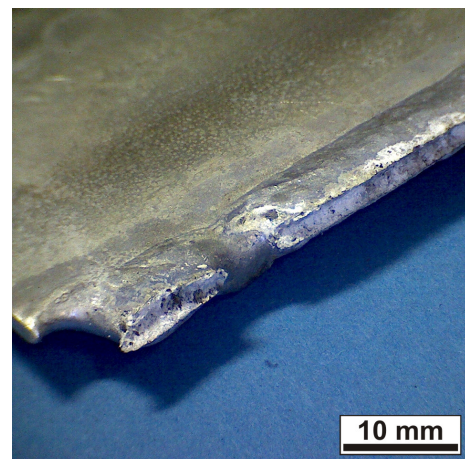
Unbeschichtetes Versuchsblech der geschweißten Verbindung AZ31 / AA6016 / AlSi12, vergrößerte Aufnahme der Bruchkante, sprödes Versagen ohne äußere mechanische Lastaufbringung nach einer Woche Korrosionsprüfung nach VDA 621-415
